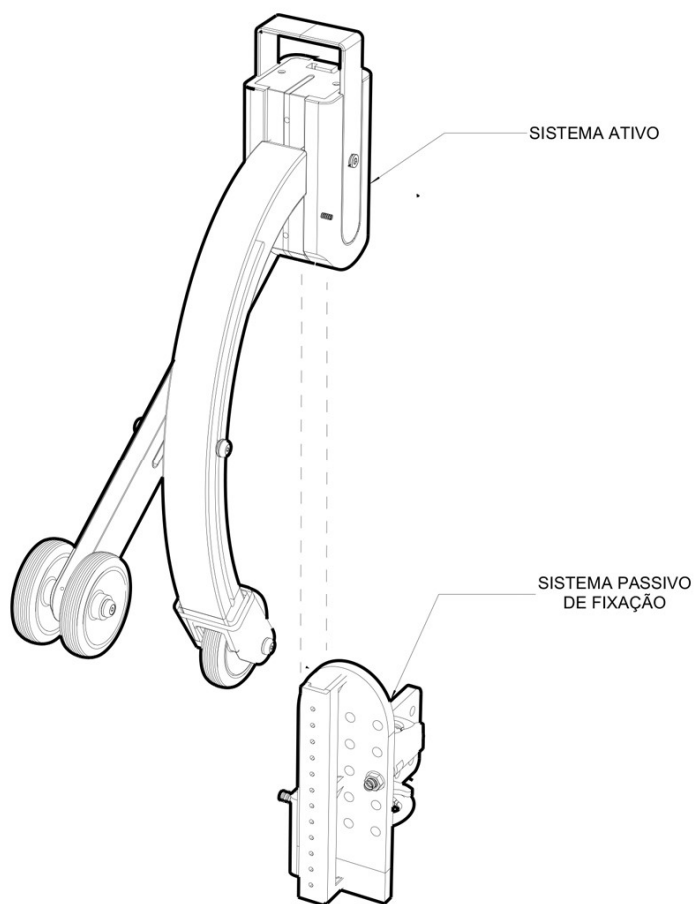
Montagem da Parte Ativa e Parte Passiva
